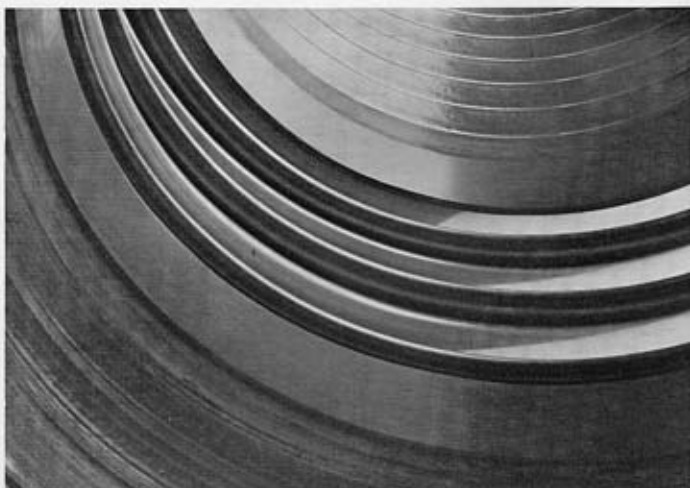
Dreiwelliger Kompensator, Innenansicht
